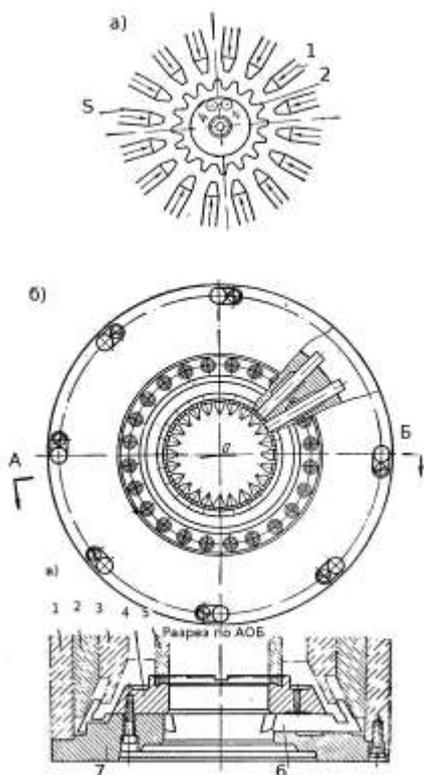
Зубодолбежная головка для нарезания прямозубых цилиндрических колес по методу копирования: а — схема процесса работы; б — общий вид зубодолбежной головки в плане; в — резцовая головка в разрезе.
